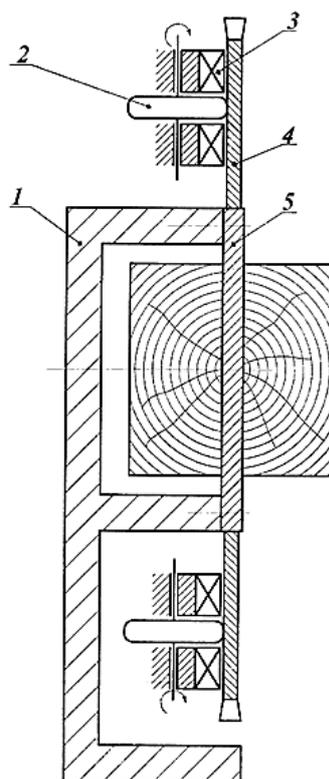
Конструкция узла резания с кольцевой пилой: 1 – станина; 2 – приводной ролик; 3 – магнит; 4 – кольцевая пила; 5 – опорный диск
